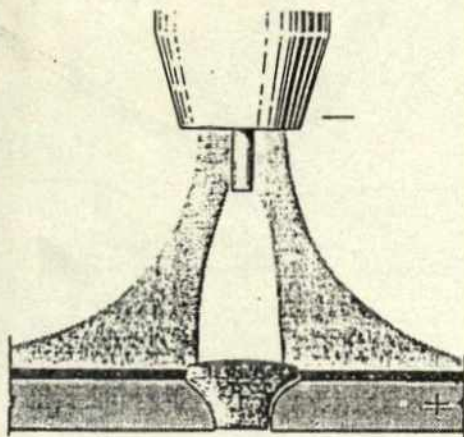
Presentación esquemática de la soldadura TIG.
